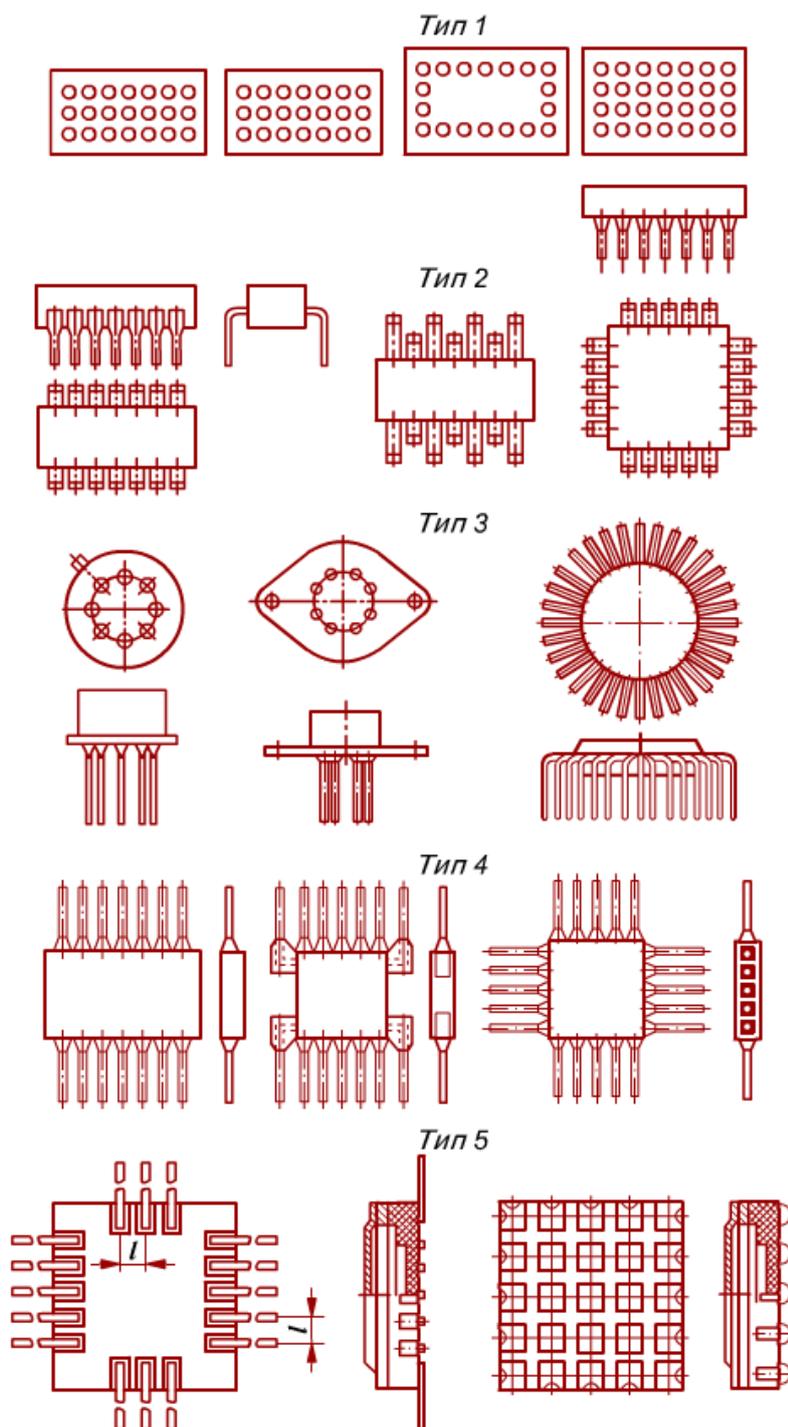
Типы корпусов ИС (1 – шаг расположения выводов)
